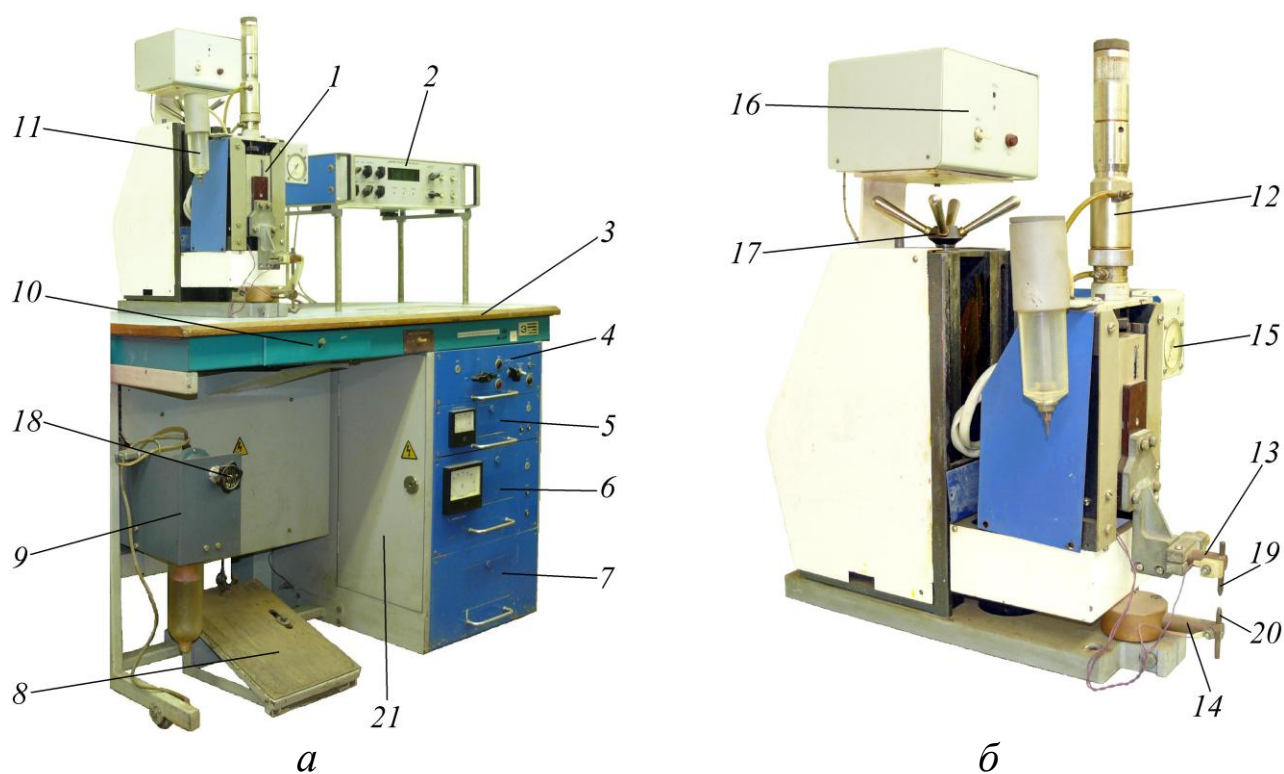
Установка УС.КТОП-6000: *а* – внешний вид; *б* - сварочная головка; 1 – блок сварочный; 2 – цифровой измеритель энергии ЦИЭ-1; 3 – стол монтажно-сборочный; 4 – блок включения; 5 – блок управления импульсом переменного тока; 6 – блок управления конденсаторным и комбинированным импульсами тока; 7 – блок конденсаторов; 8 – педаль; 9 – пневмопанель; 10 – коммутатор; 11 – капельница; 12 – пневмоцилиндр; 13 – электрододержатель верхний; 14 – электрододержатель нижний; 15 – манометр; 16 – блок управления капельницей; 17 – маховичок пружинного привода сжатия; 18 – регулятор (редуктор) давления воздуха; 19 – электрод верхний; 20 – электрод нижний; 21 – шкаф
